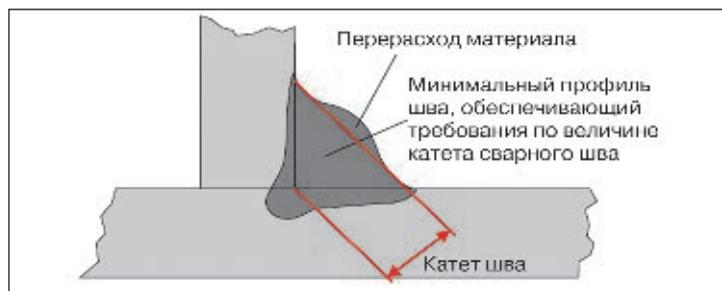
Перерасход сварочной проволоки при сварке в чистом CO_2 — для заданного катета шва
